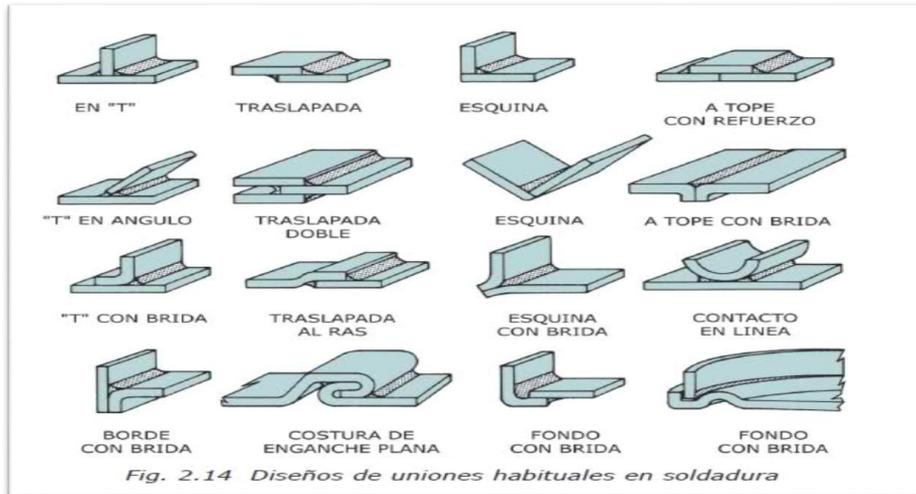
Diseños de uniones habituales en soldadura.
